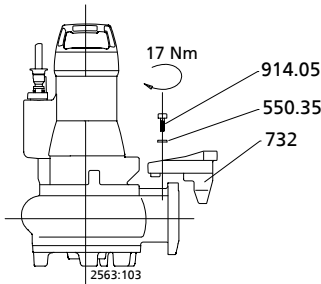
Montaje del soporte con guía del cable, 1 barra guía y estribo guía
